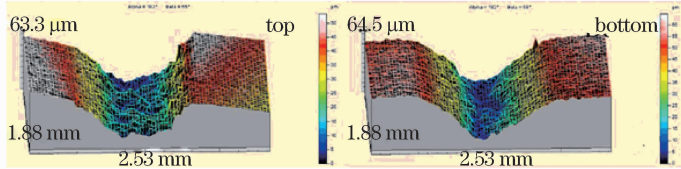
脉冲式 Nd:YAG 焊接接头的 3D 轮廓图像分析图。Top 为上表面, bottom 为下表面
